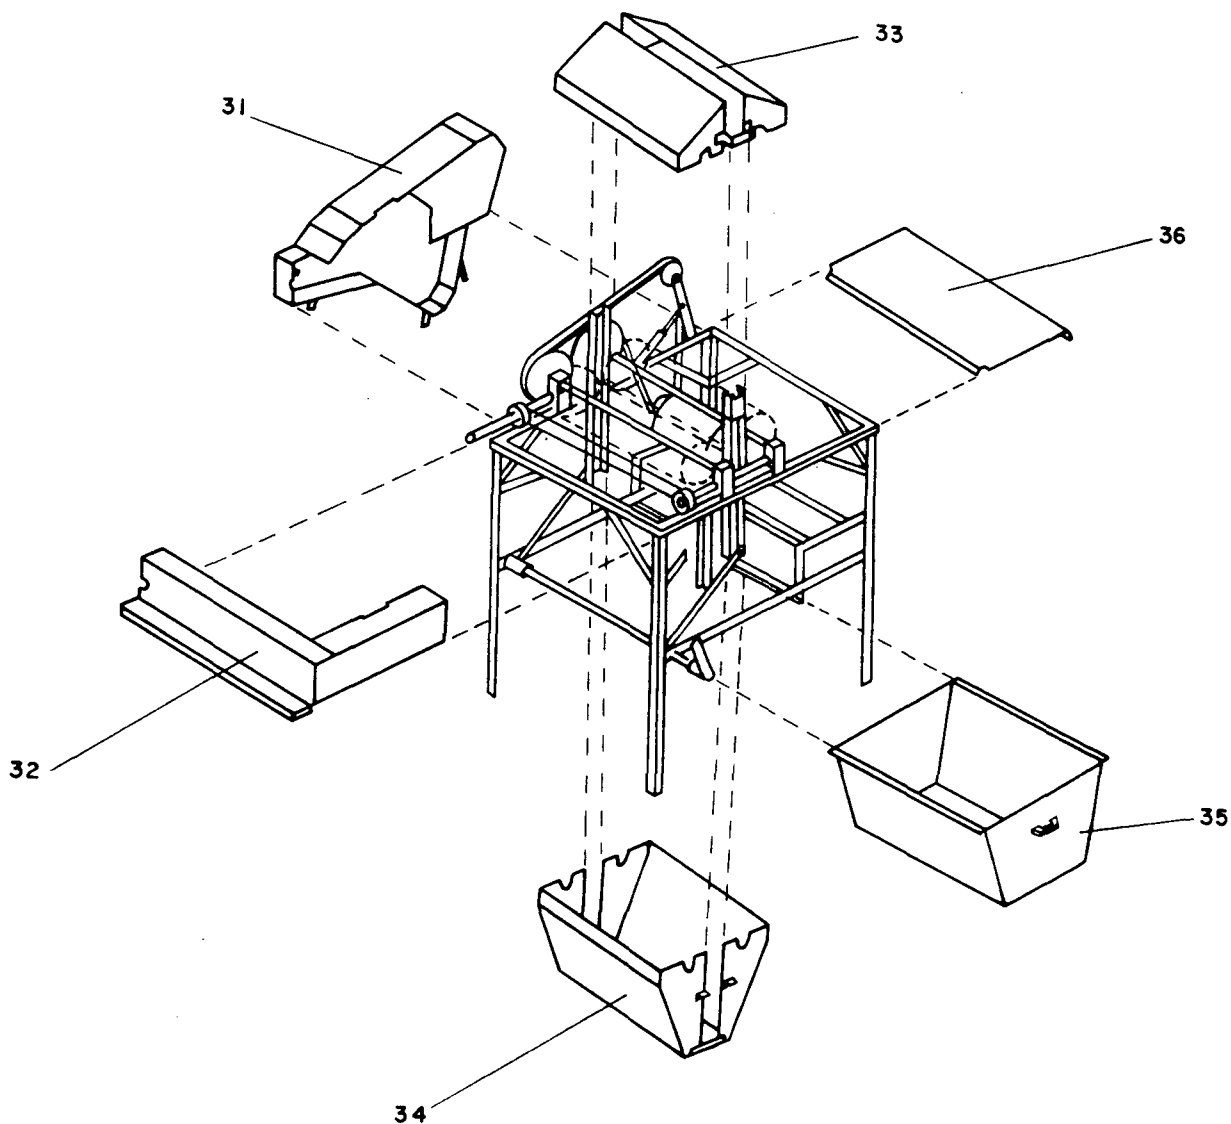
Vista explodida dos conjuntos de proteção.
